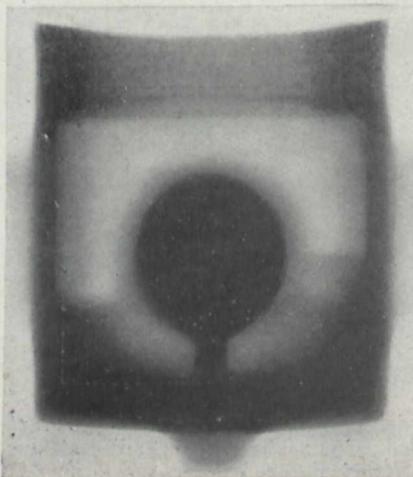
(rechts). Röntgenshattenbild eines autogen geschweißten Aluminiumgehäuses. Die hellen Stellen in der Schweißnaht sind Fehlstellen. Die hier vorhandenen Hohlräume beeinträchtigen die Güte der Schweißung stark. (Originalgröße.)
